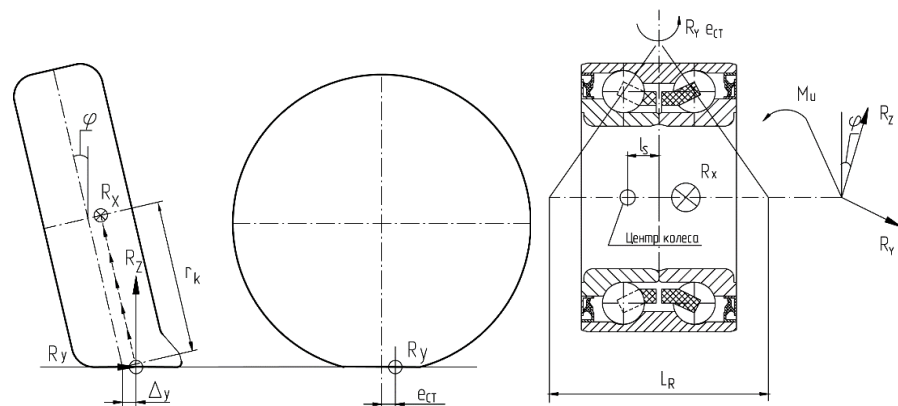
Схема сил, действующих на колесо и ступичный подшипник
